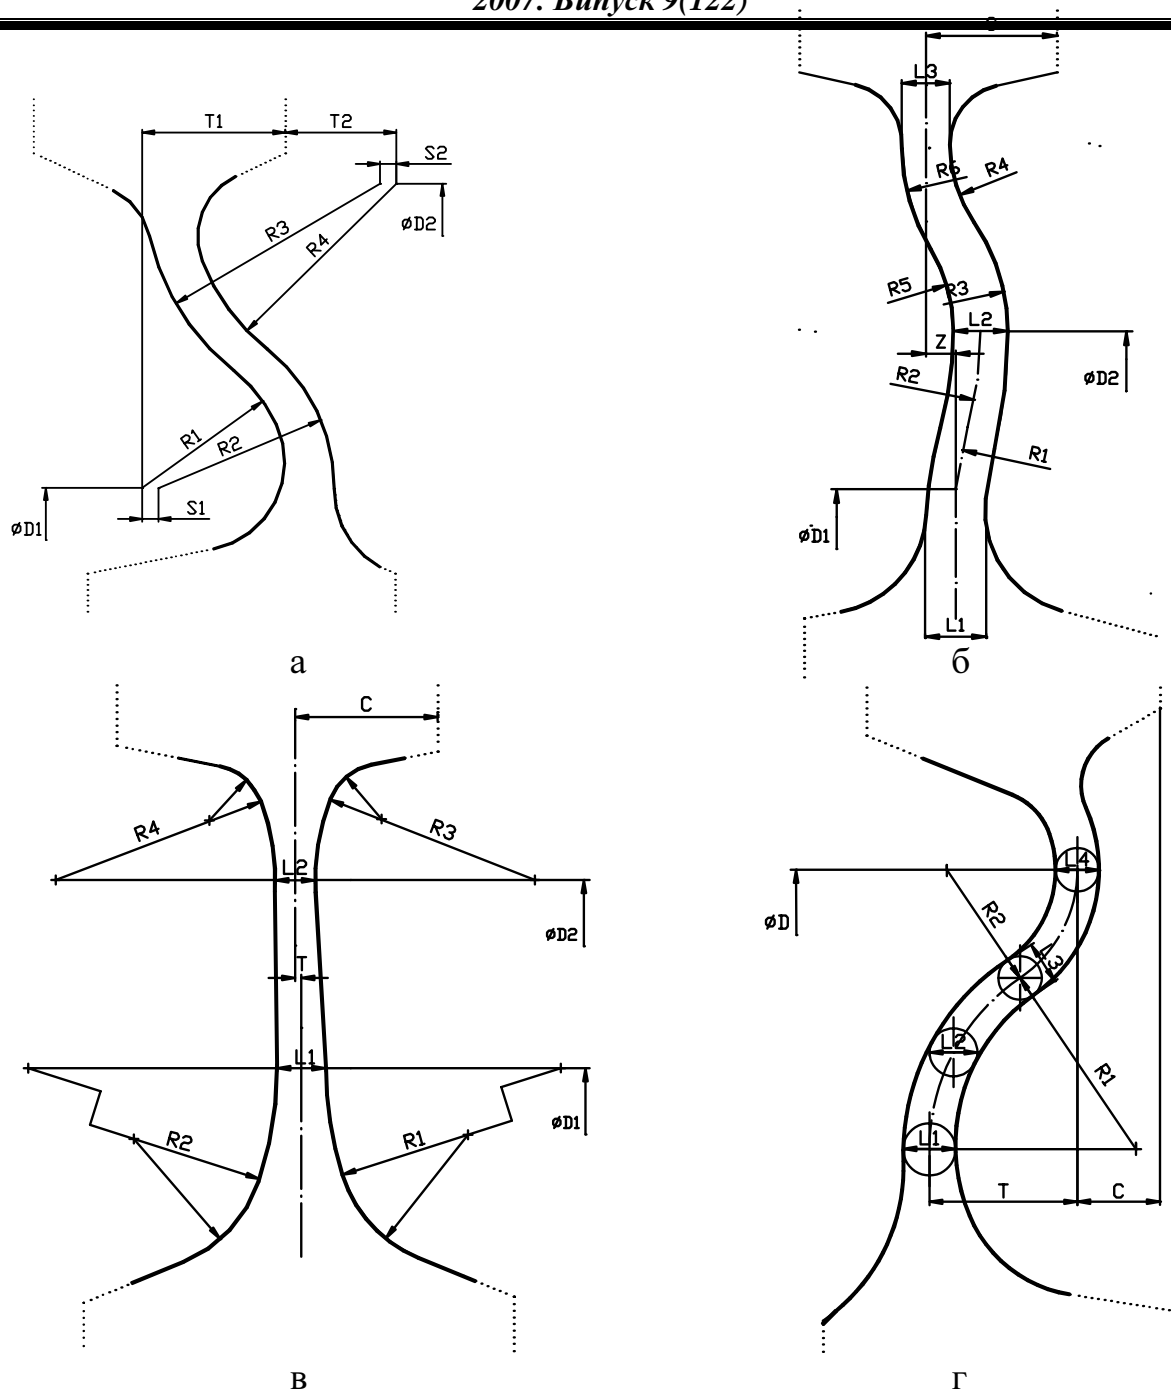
Схемы дисков для профилей колес 4-го типа
